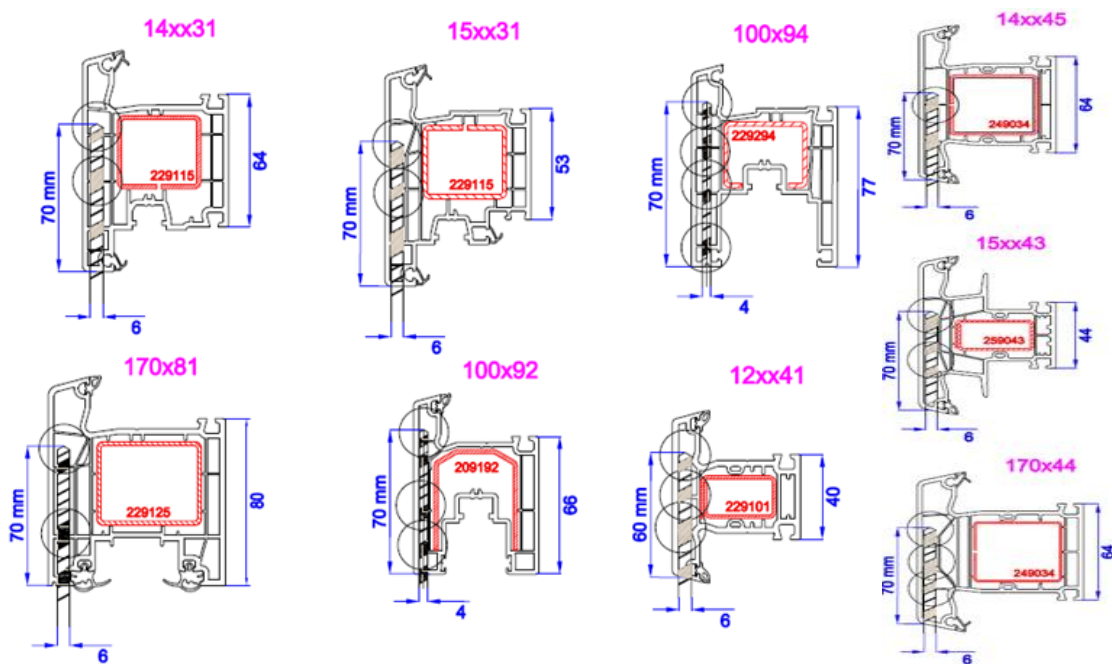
Representação da furação em cada tipo de perfil de travessa.
